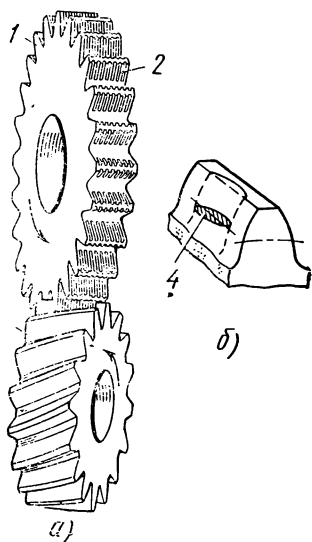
Схема шевингования зубьев колеса дисковым шевером:
